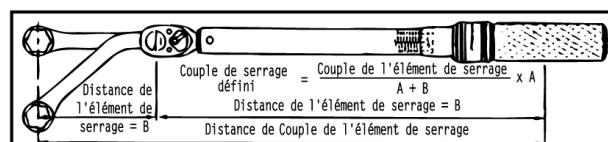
Le couple de l'élément de serrage est supérieur au couple de serrage du Carré d'entraînement de la clé dynamométrique.
